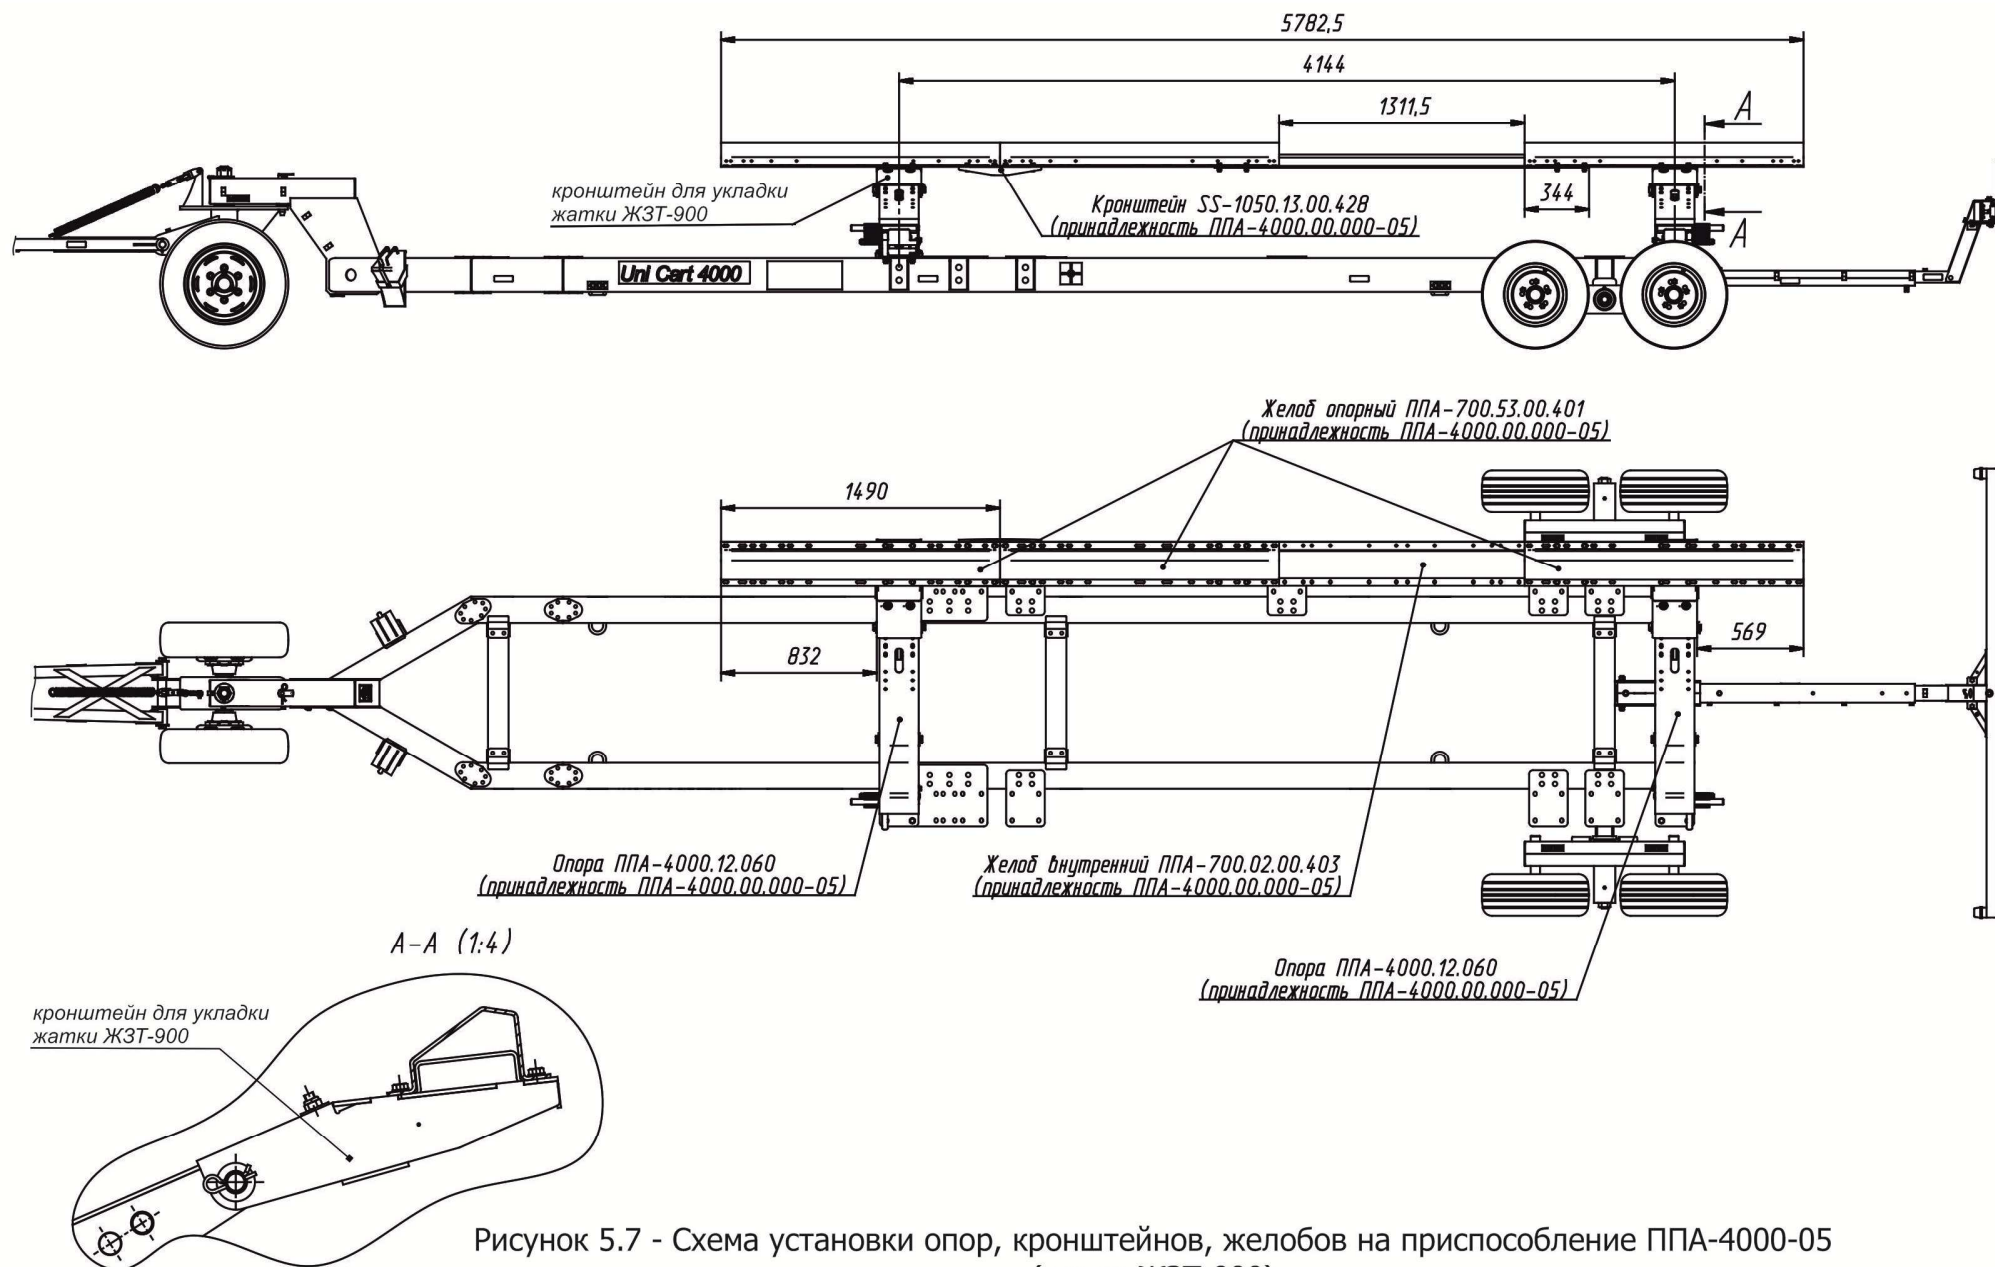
Схема установки опор, кронштейнов, желобов на приспособление ППА-4000-05 (жатка ЖЗТ-900)
